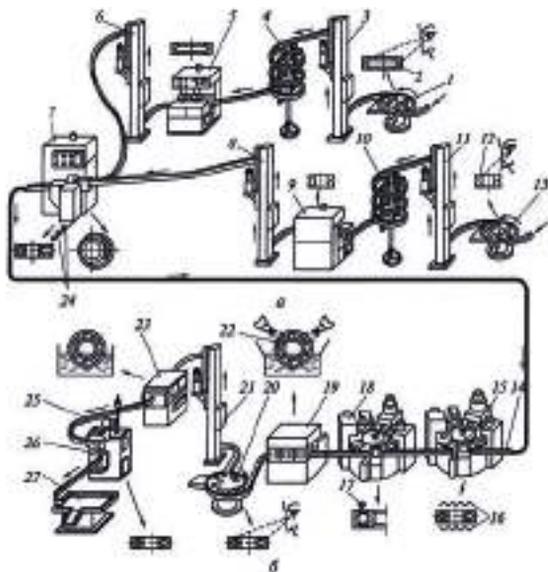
АЛ для сборки, контроля и упаковки шарикоподшипников:
